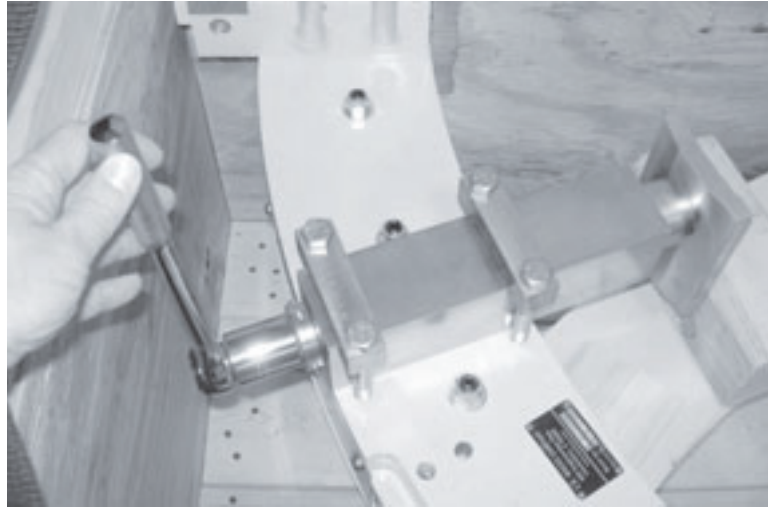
Поворачивайте регулировочные винты зажимных механизмов для фиксации станка на заготовке.
